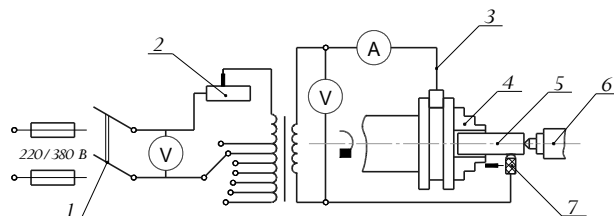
Принципова схема електромеханічної обробки на токарному верстаті:
